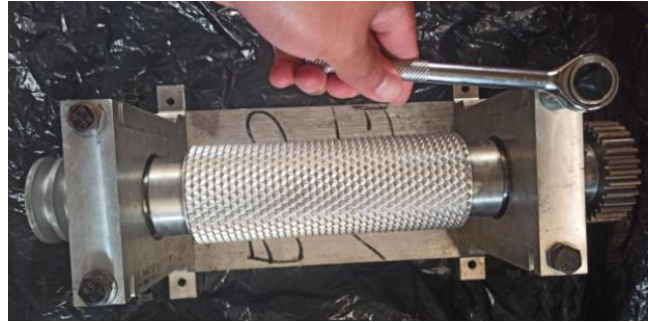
Ajuste de la base superior del rodillo para el estampado.
